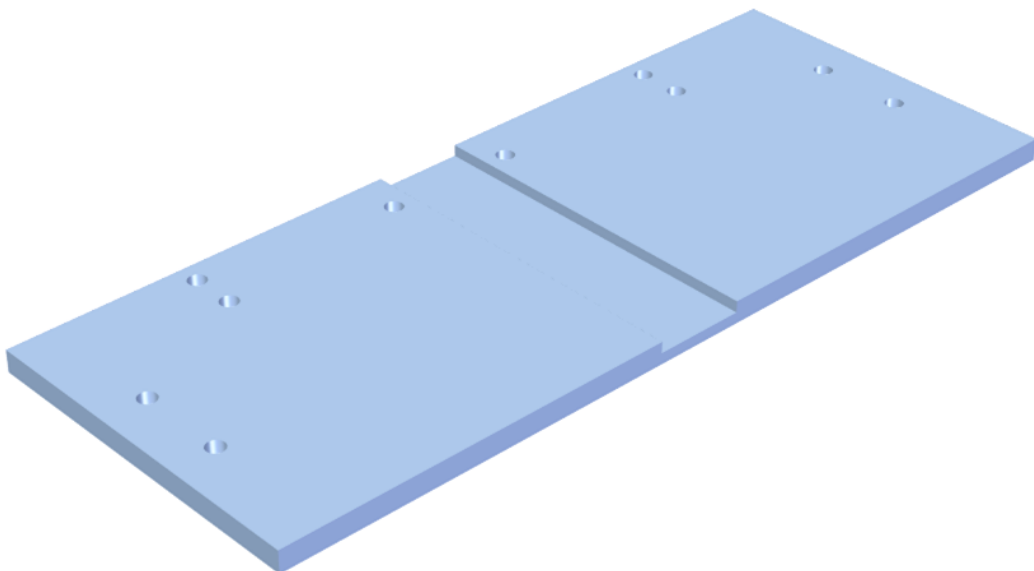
Placa base, esta pieza es la base del mecanismo y en ella se ensamblan piezas del sistema de avance seleccionado.
